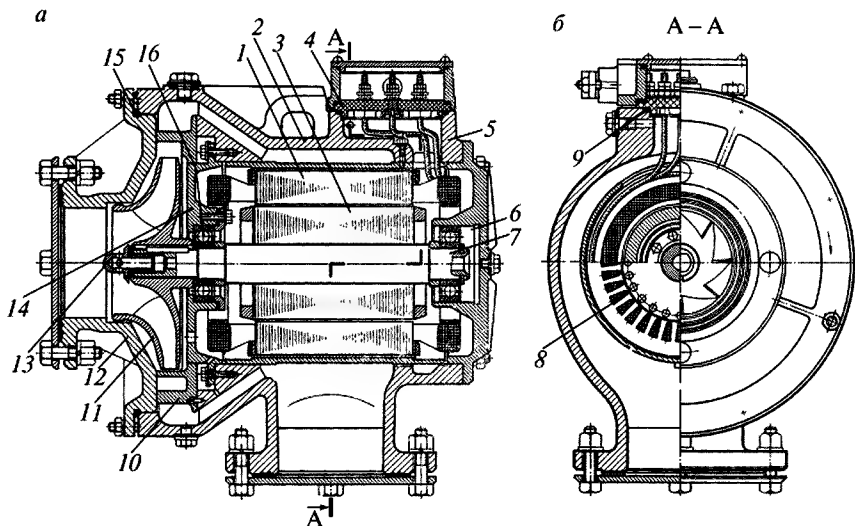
Продольный (а) и поперечный (б) разрезы электронасоса 4ТТ63/10: 1 – статор; 2 – корпус; 3 – ротор; 4 – коробка выводов; 5, 14 – подшипниковые шиты; 6, 16 – якорные подшипники; 7 – вал; 8 – обмотка статора; 9 – панель выводов; 10 – направляющий аппарат; 11 – рабочее колесо; 12 – всасывающий патрубок; 13 – обтекатель; 15 – уплотнительное кольцо
